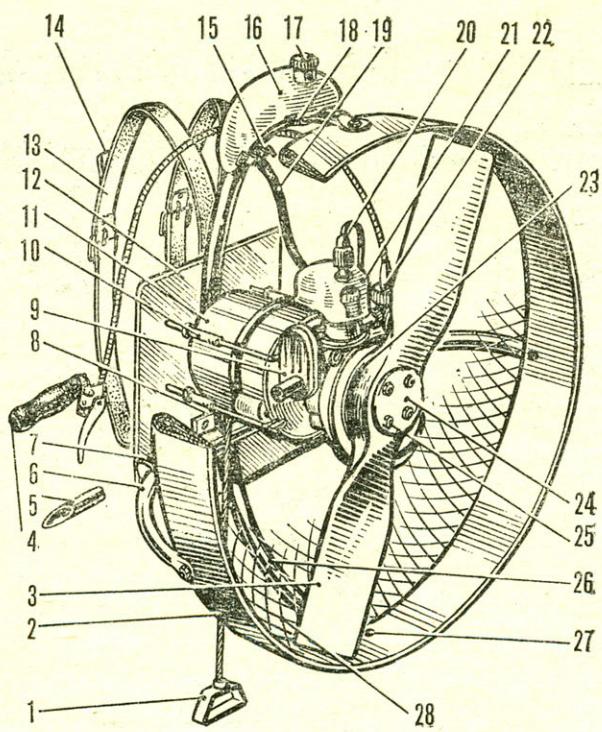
Ранцевый аэродвигатель МПИ-4: 1 — ручка и трос стартера, 2 — кольцо, 3 — воздушный винт, 4 — ручка и рычаг управления, 5 — выхлопная труба, 6 — горизонтальная дуга кольца, 7 — хомут крепления выхлопной трубы, 8 — бобышка, 9 — глушитель, 10 — винтовые стяжки, 11 — проставка, 12 — опорная плита, 13, 14 — плечевые ремни, 15 — топливный кран, 16 — бак, 17 — горловина бака, 18 — хомут крепления бака, 19 — бензопровод, 20 — свеча, 21 — двигатель, 22 — карбюратор, 23 — фланцевая муфта, 24 — фланец, 25 — болт с гайкой, 26 — вертикальная дуга кольца, 27 — болт с гайкой, 28 — защитная сетка,
